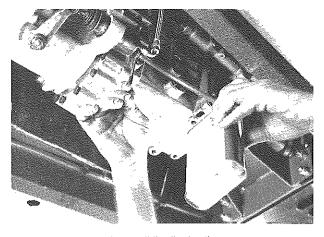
Fissaggio del tubo flessibile alla vite di spurgo Connecting a flex pipe to drain plug
